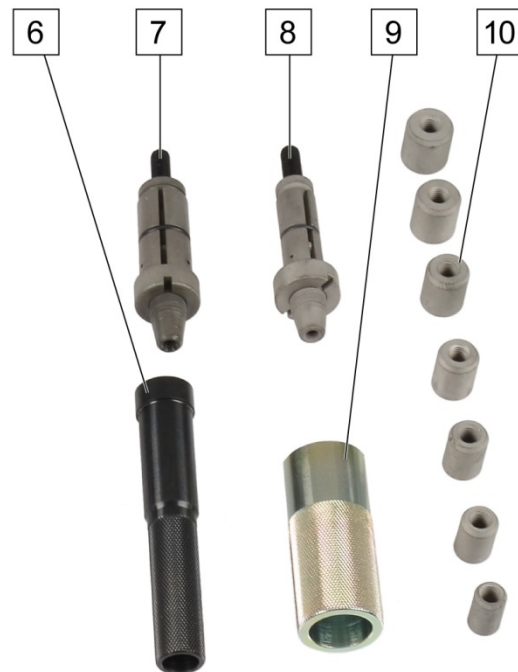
Axe de guidage, broches de serrage, clé fendue, pièces de guidage
